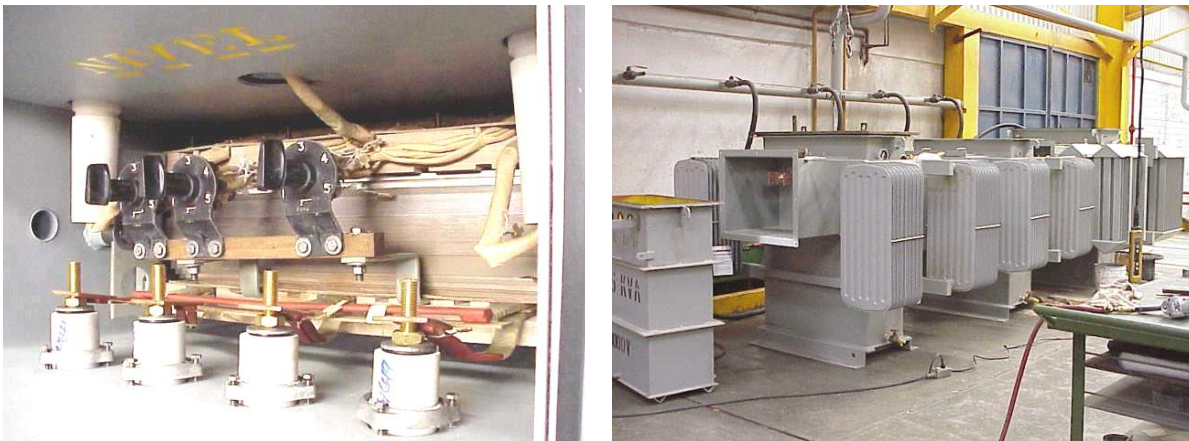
Conjunto interno en tanque y llenado de aceite.
